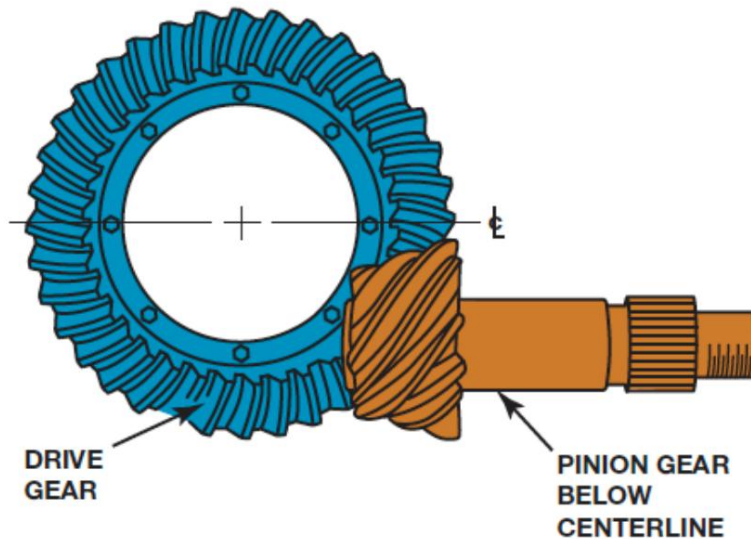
Conjunto de engranajes hipoides. Los engranajes forman un conjunto acoplado y deben reemplazarse como un conjunto.
